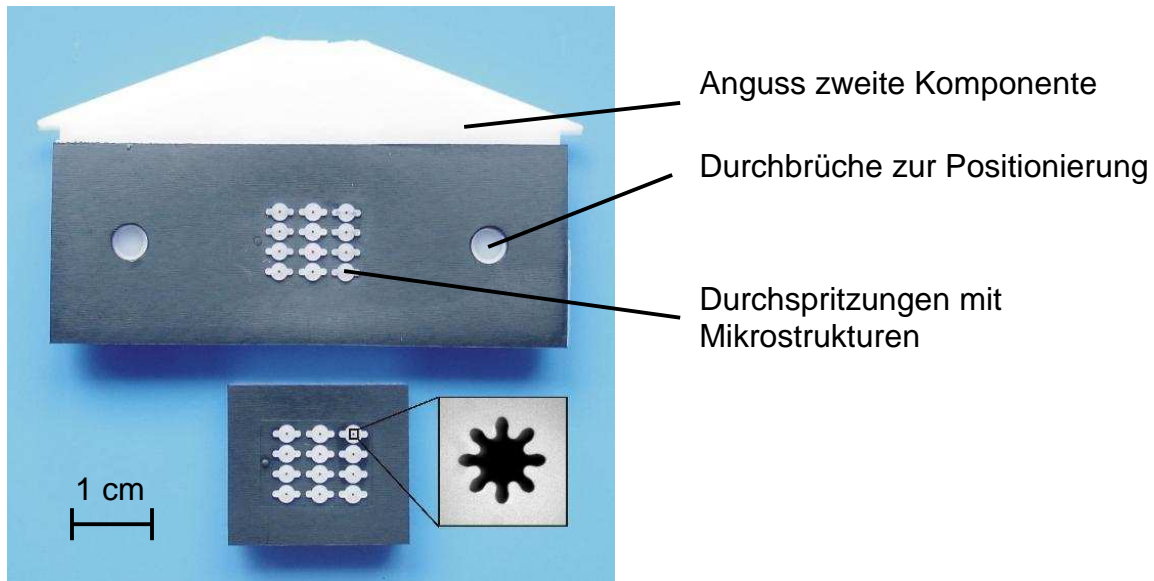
Oben: Einlegeteil aus PA12-C, hinterspritzt mit POM, unten: Ausschnitt für die Galvanoformung
